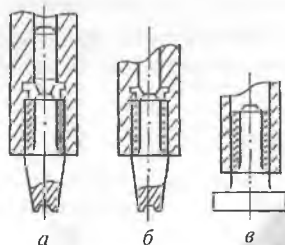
Конструкция обжимок пневматического молотка: а — для клепки заклепок с полукруглой головкой; б — с плоской выступающей головкой; в — для клепки потайных заклепок и для прямой клепки
